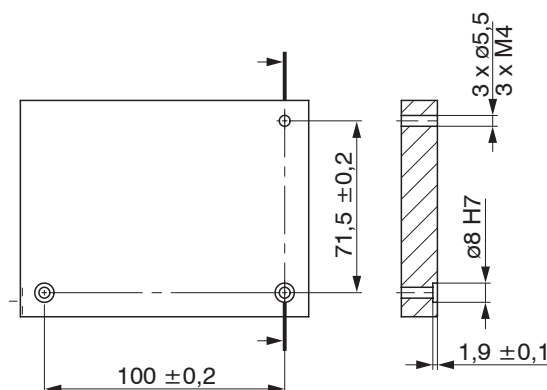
Maßzeichnung Montagebohrungen, Maße in mm, nicht maßstabsgetreu
